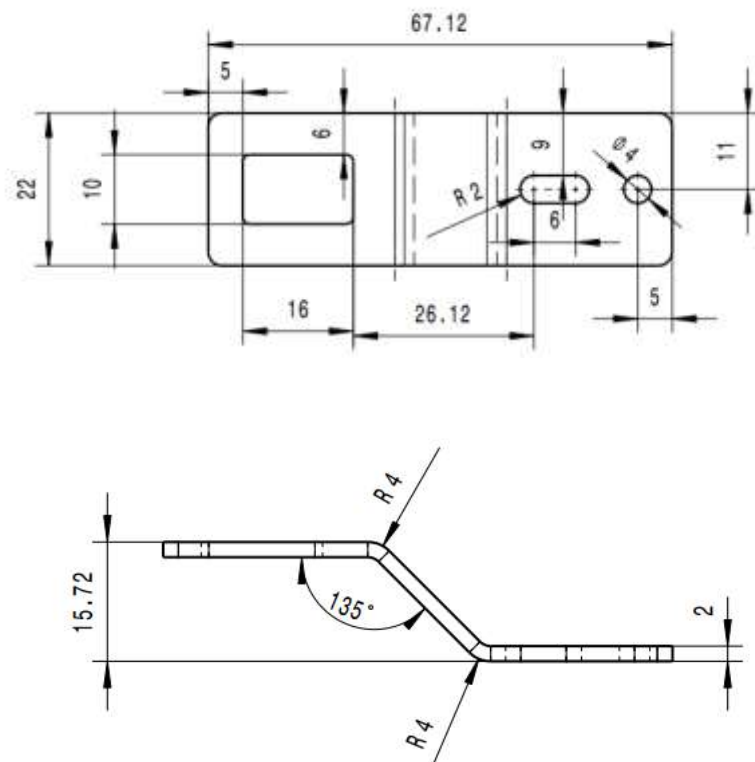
Planta y alzado de la pieza a diseñar (Fuente propia – CATIA)
